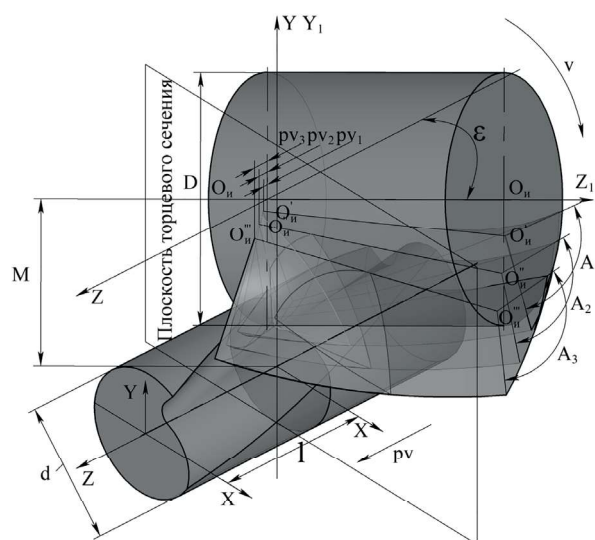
Определение размеров срезаемого слоя при фрезеровании винтовой поверхности фрезой стандартного профиля
